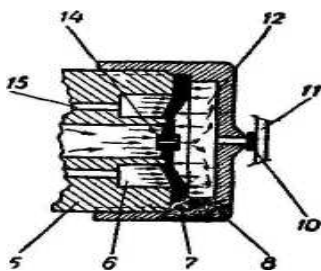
Схема работы клапанного механизма, легочного автомата: 5 — обойма; 6 — воздушная полость; 7 — мембрана; 8 — накидная гайка; 10 — воздушный клапан; 11 — пластина; 12 — затворная полость; 14 — втулка; 15 — воздушный канал.
